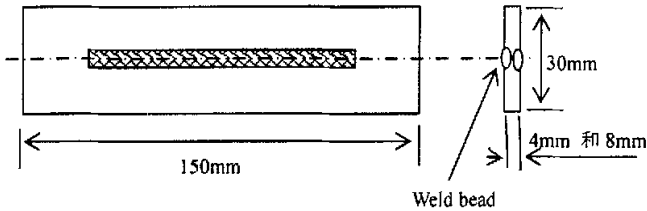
304L 不锈钢焊接试样尺寸
